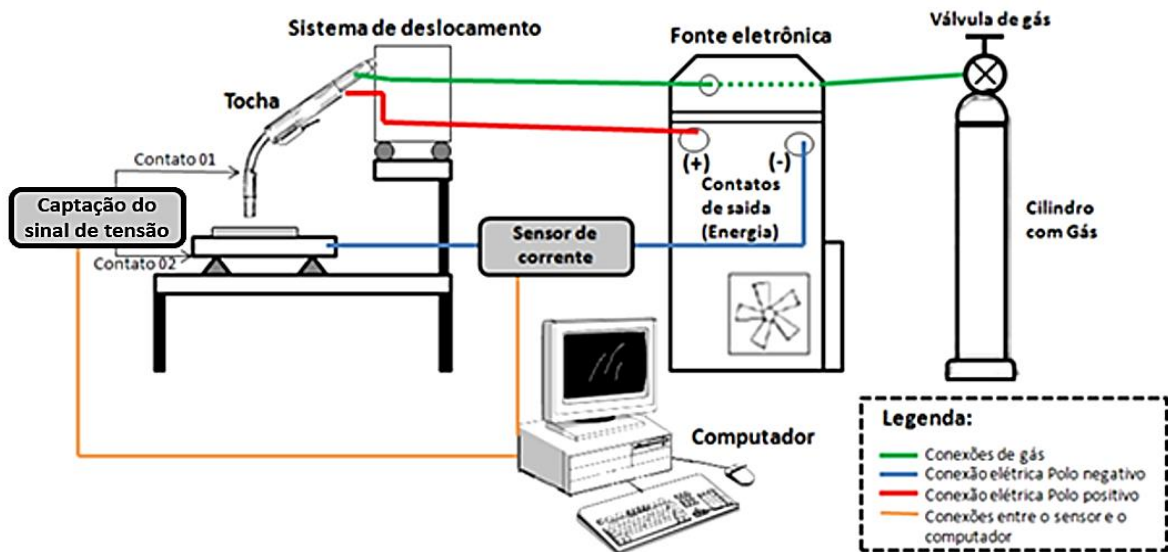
Representação esquemática da montagem experimental para as soldagens A-MIG/MAG.
